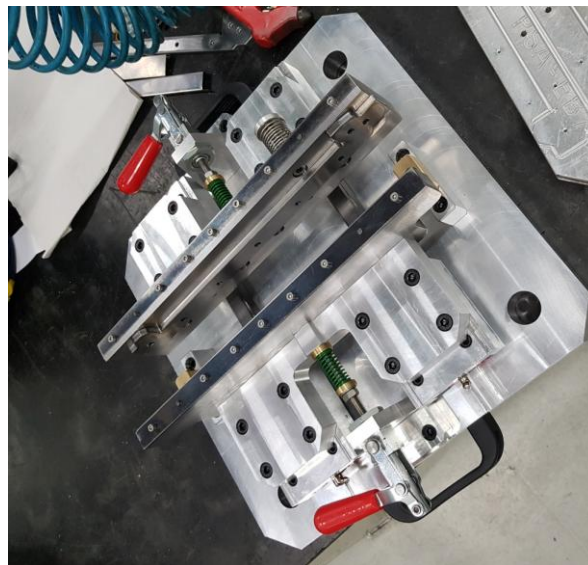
Utillaje de soldadura láser de tubos de refrigeración de gases
